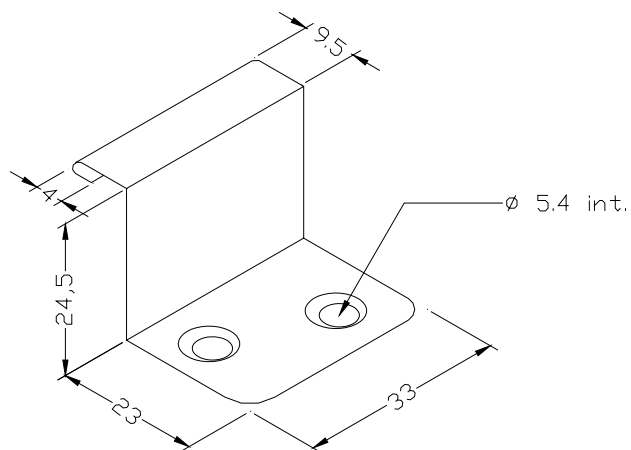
Toiture Structurale support béton (fixation par clou-cheville)
